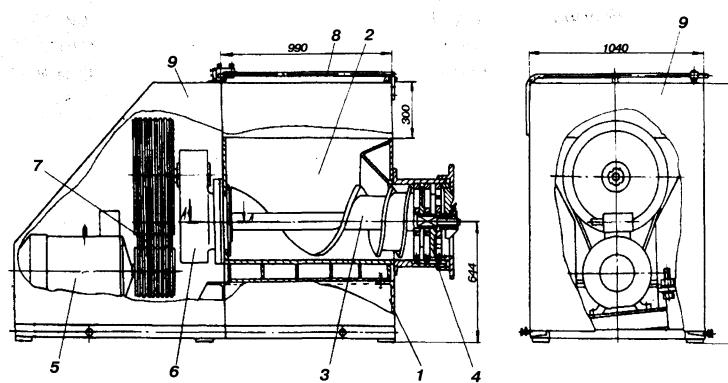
Волчок-дробилка В2-ФДБ2-Б:
